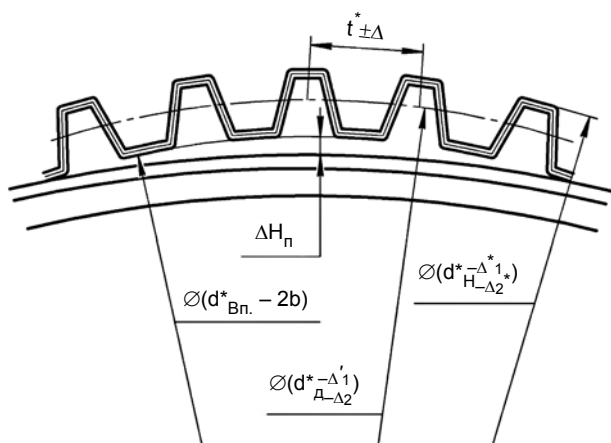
Схема обеспечения точности сборки корпуса шестерни и зубчатого сектора
